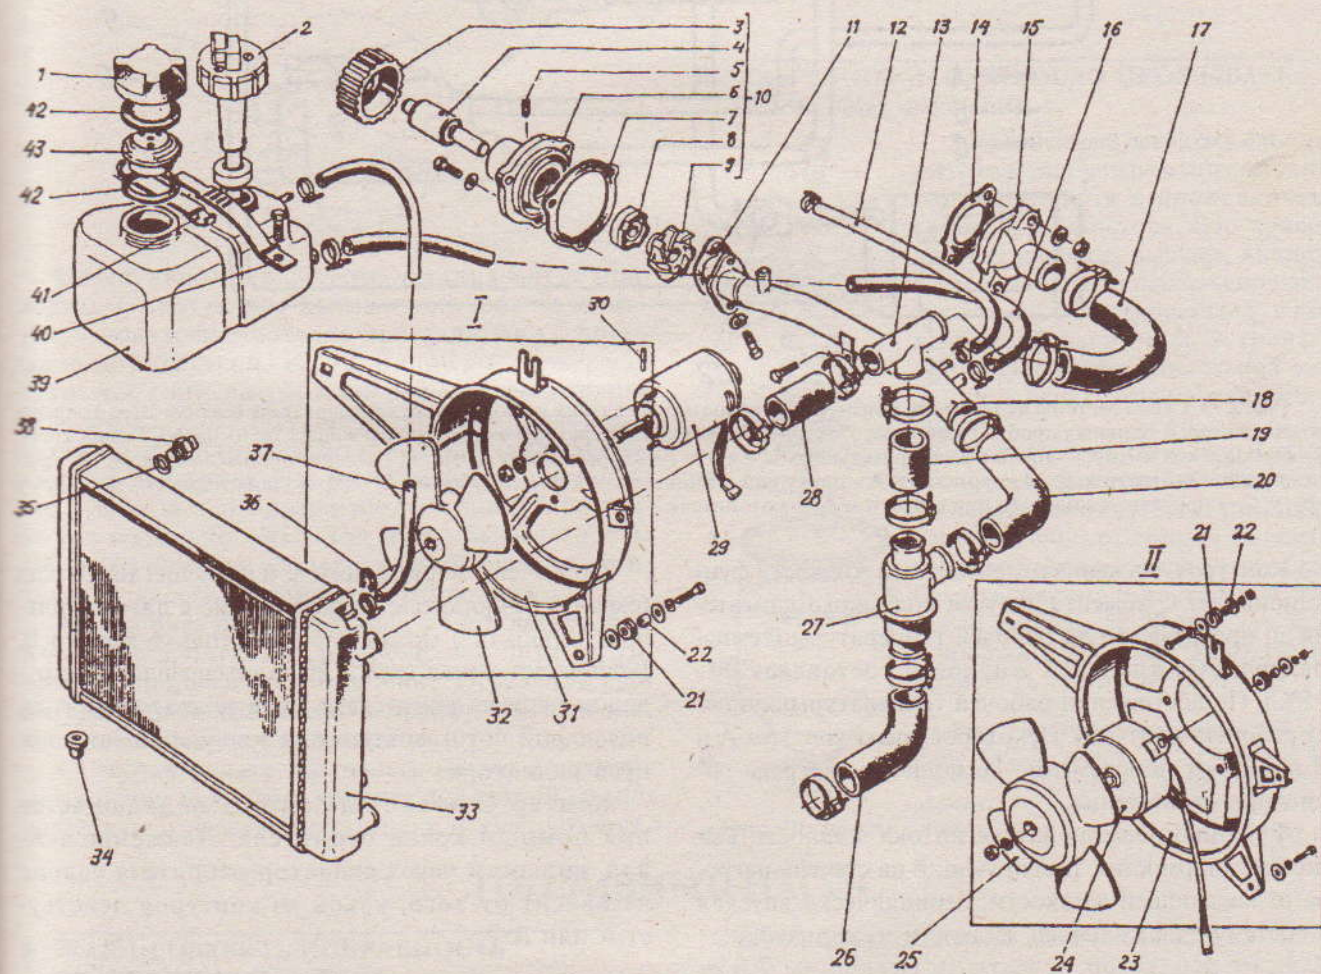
Детали системы охлаждения двигателя: 1 - корпус пробки; 2 - датчик уровня охлаждающей жидкости; 3 - шкив привода насоса; 4 - подшипник в сборе с валом; 5 - винт стопорный; 6 - корпус насоса; 7 - прокладка; 8 - манжета уплотнительная; 9 - крыльчатка; 10 - насос в сборе; 11 - прокладка; 12 - шланг к радиатору отопителя; 13 - тройник; 14 - прокладка; 15 - патрубок; 16 - шланг к расширительному бачку; 17 - шланг подводящий; 18 - труба перепускная; 19 - верхний шланг термостата; 20 - шланг от термостата к перепускной трубе; 21 - втулка; 22 - втулка дистанционная; 23 - кожух электродвигателя; 24 - электродвигатель 90 Вт; 25 - крыльчатка; 26 - шланг отводящий; 27 - термостат; 28 - шланг радиатора; 29 - электродвигатель 40 Вт; 30 - штифт; 31 - кожух ventильатора; 32 - крыльчатка; 33 - радиатор; 34 - втулка; 35 - прокладка; 36 - фиксатор; 37 - шланг пароотводящий; 38 - датчик включения электроventильатора; 39 - бачок расширительный; 40 - лента передняя; 41 - лента задняя; 42 - прокладка; 43 - блок клапанов; I - установка электродвигателя мощностью 40 Вт; II - установка электродвигателя мощностью 90 Вт
